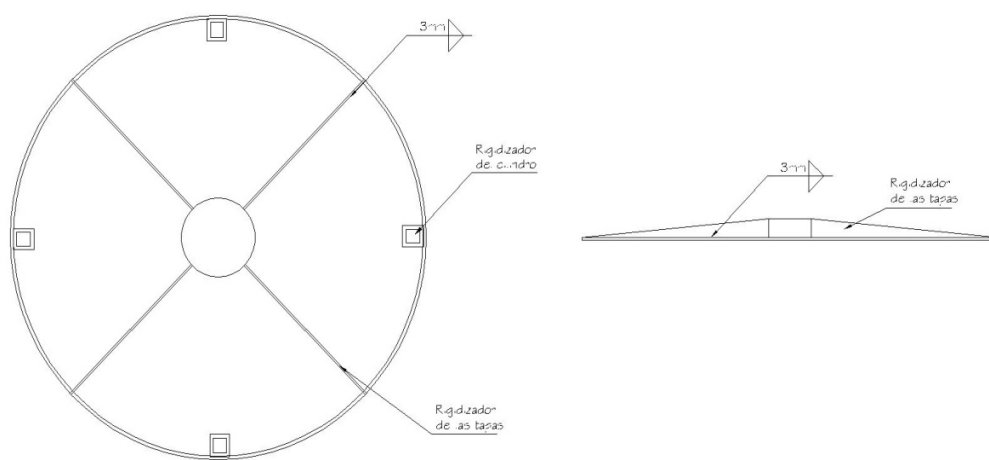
Detalle 2 de soldadura para tapas del cilindro.
